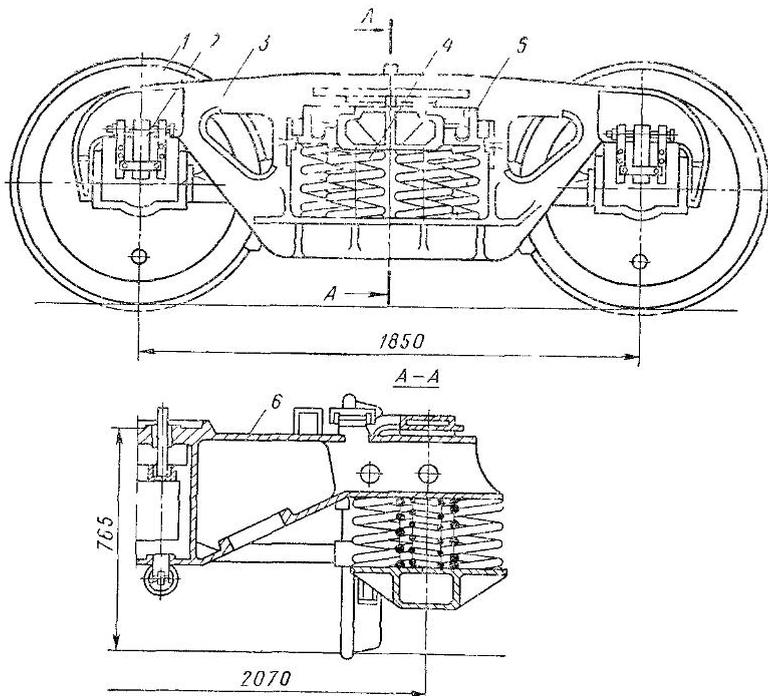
Тележка усиленной конструкции на подшипниках скольжения
